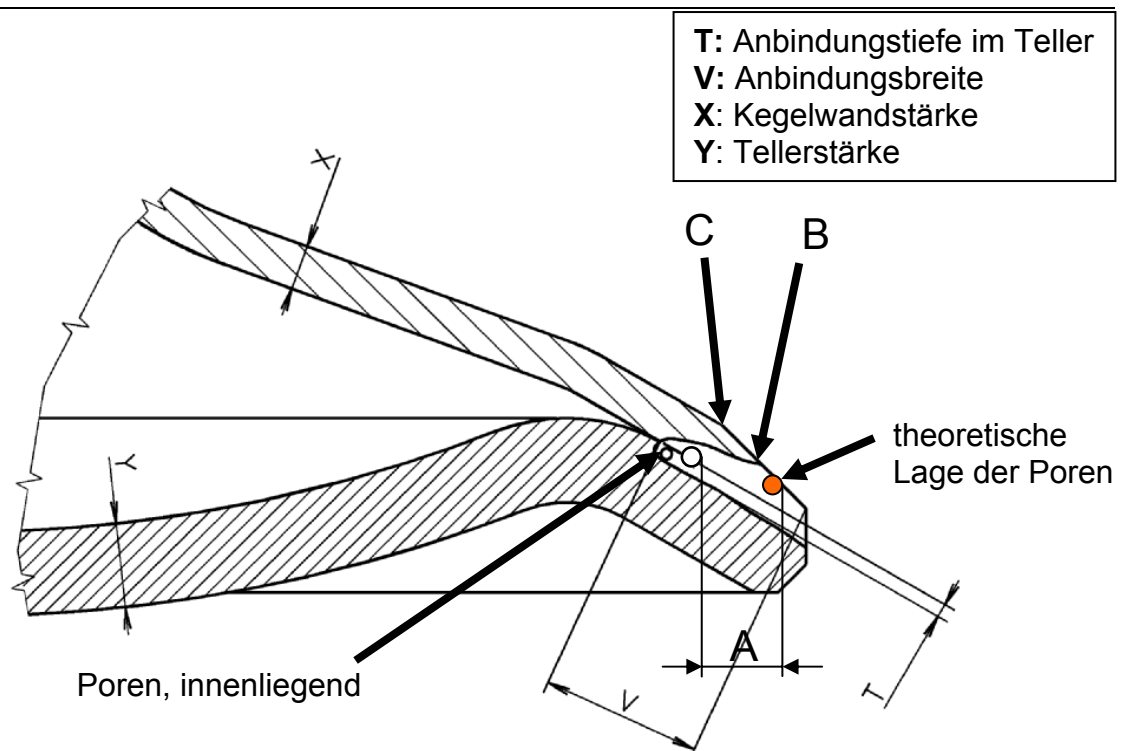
ZB2; Schweißdefinition Teller/Kegel; bearbeitete Form
